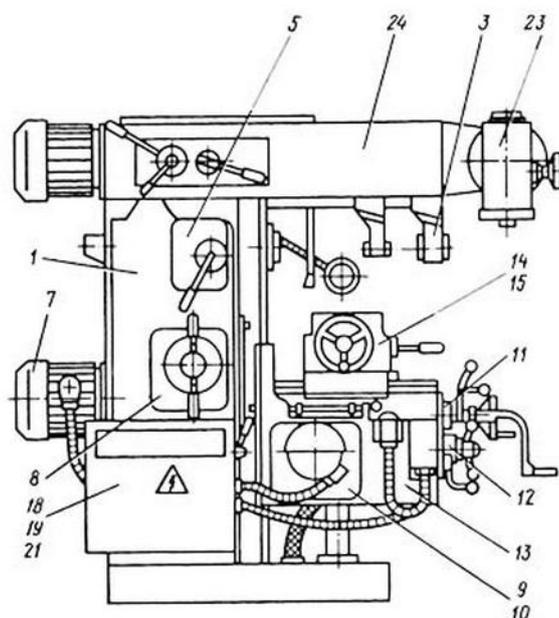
Схема вертикально-фрезерного станка БР81Г
